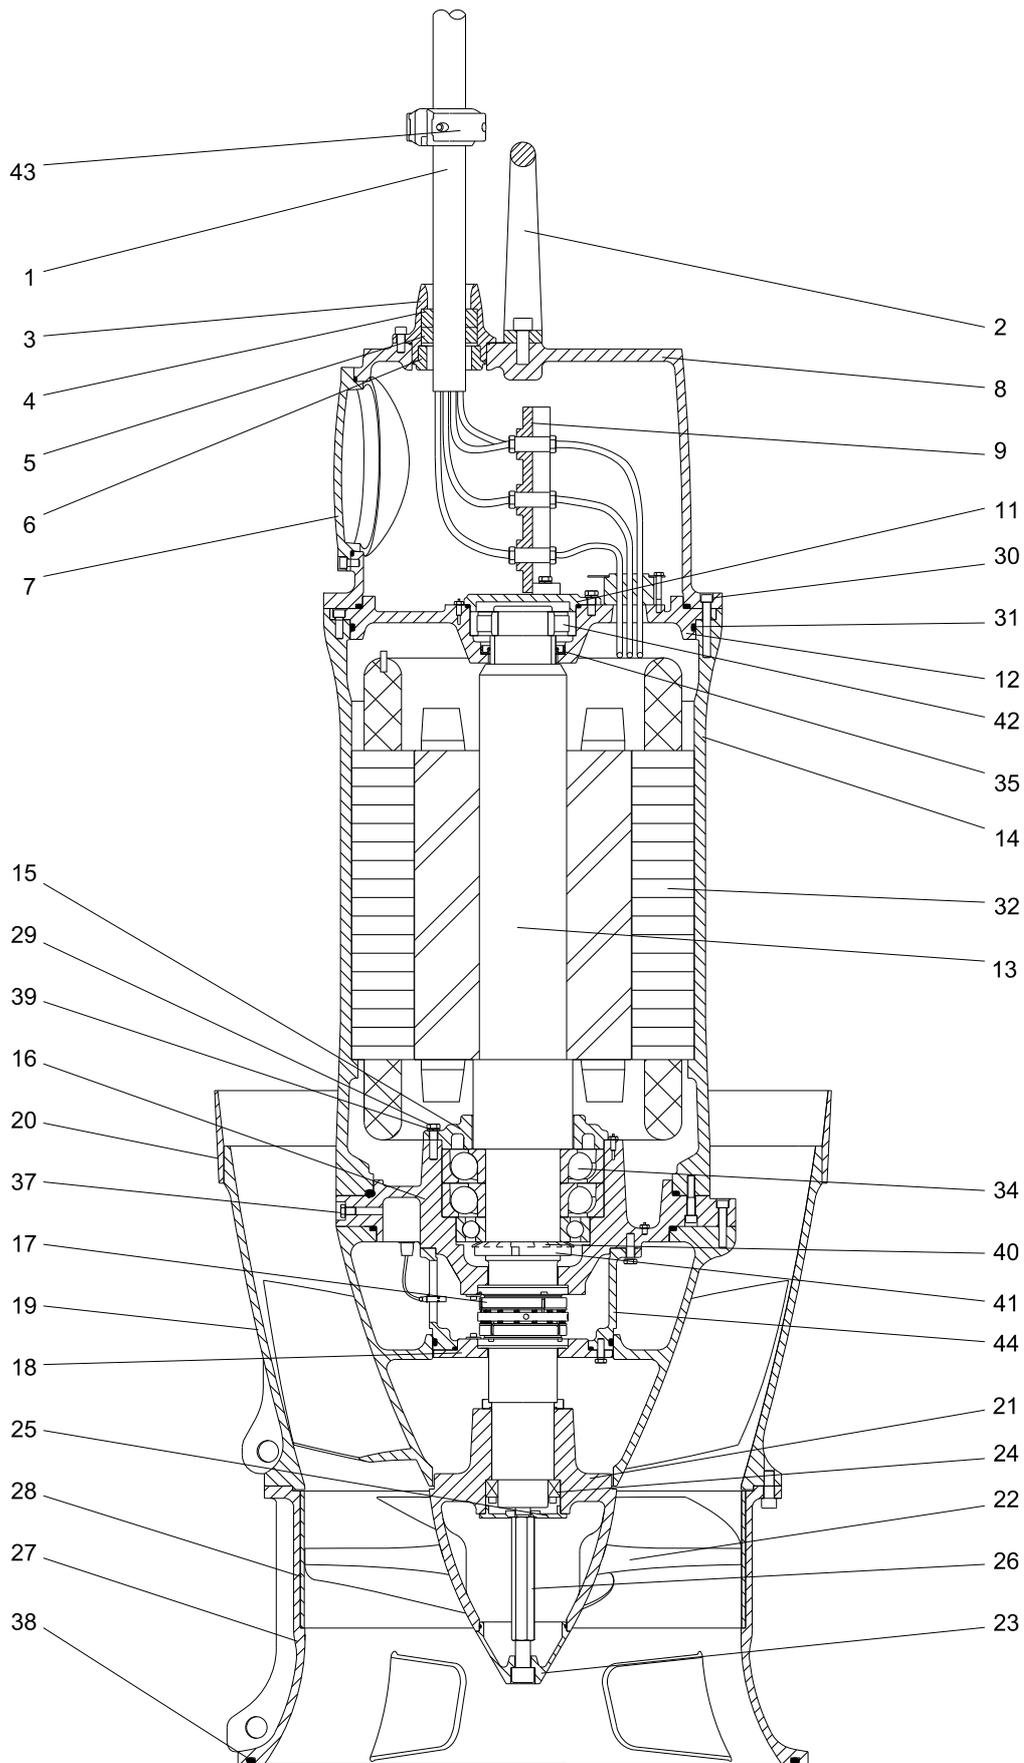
Чертеж в разрезе, КРЛ, обсадная труба диаметром 1000-1800
